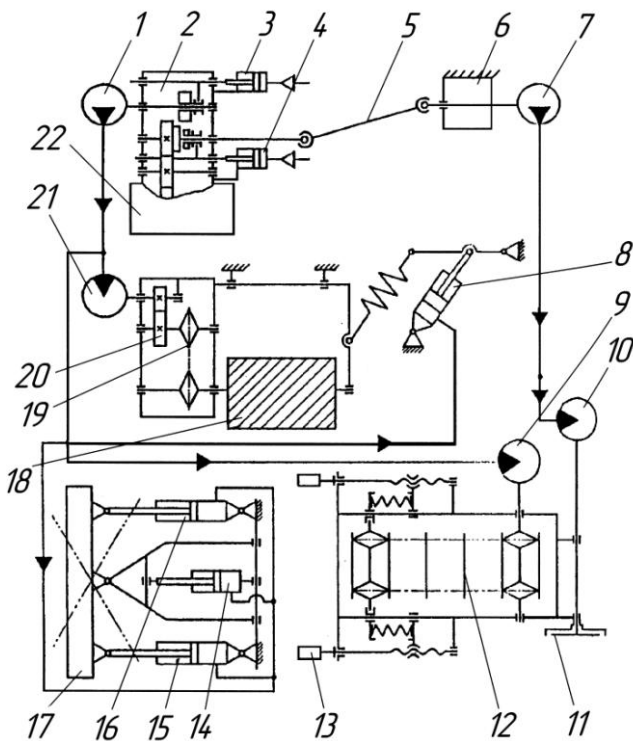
Кинематическая схема комбинированной машины:
